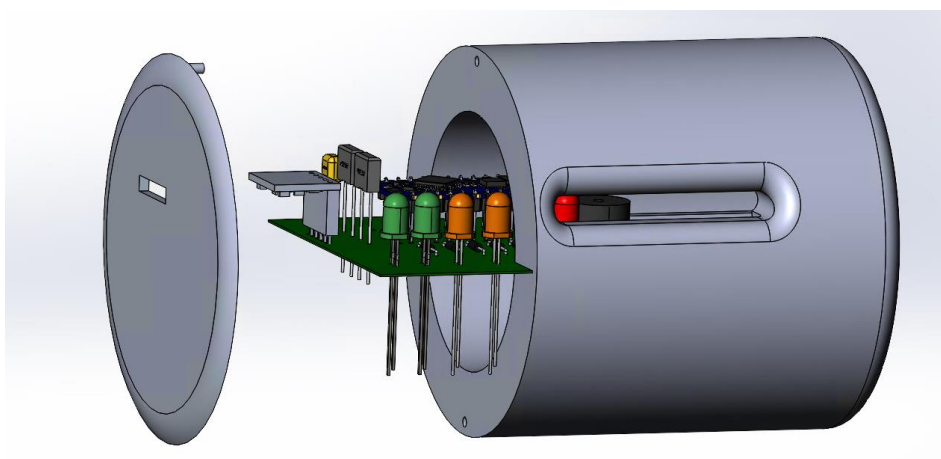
Розміщення друкованої плати всередині корпусу
